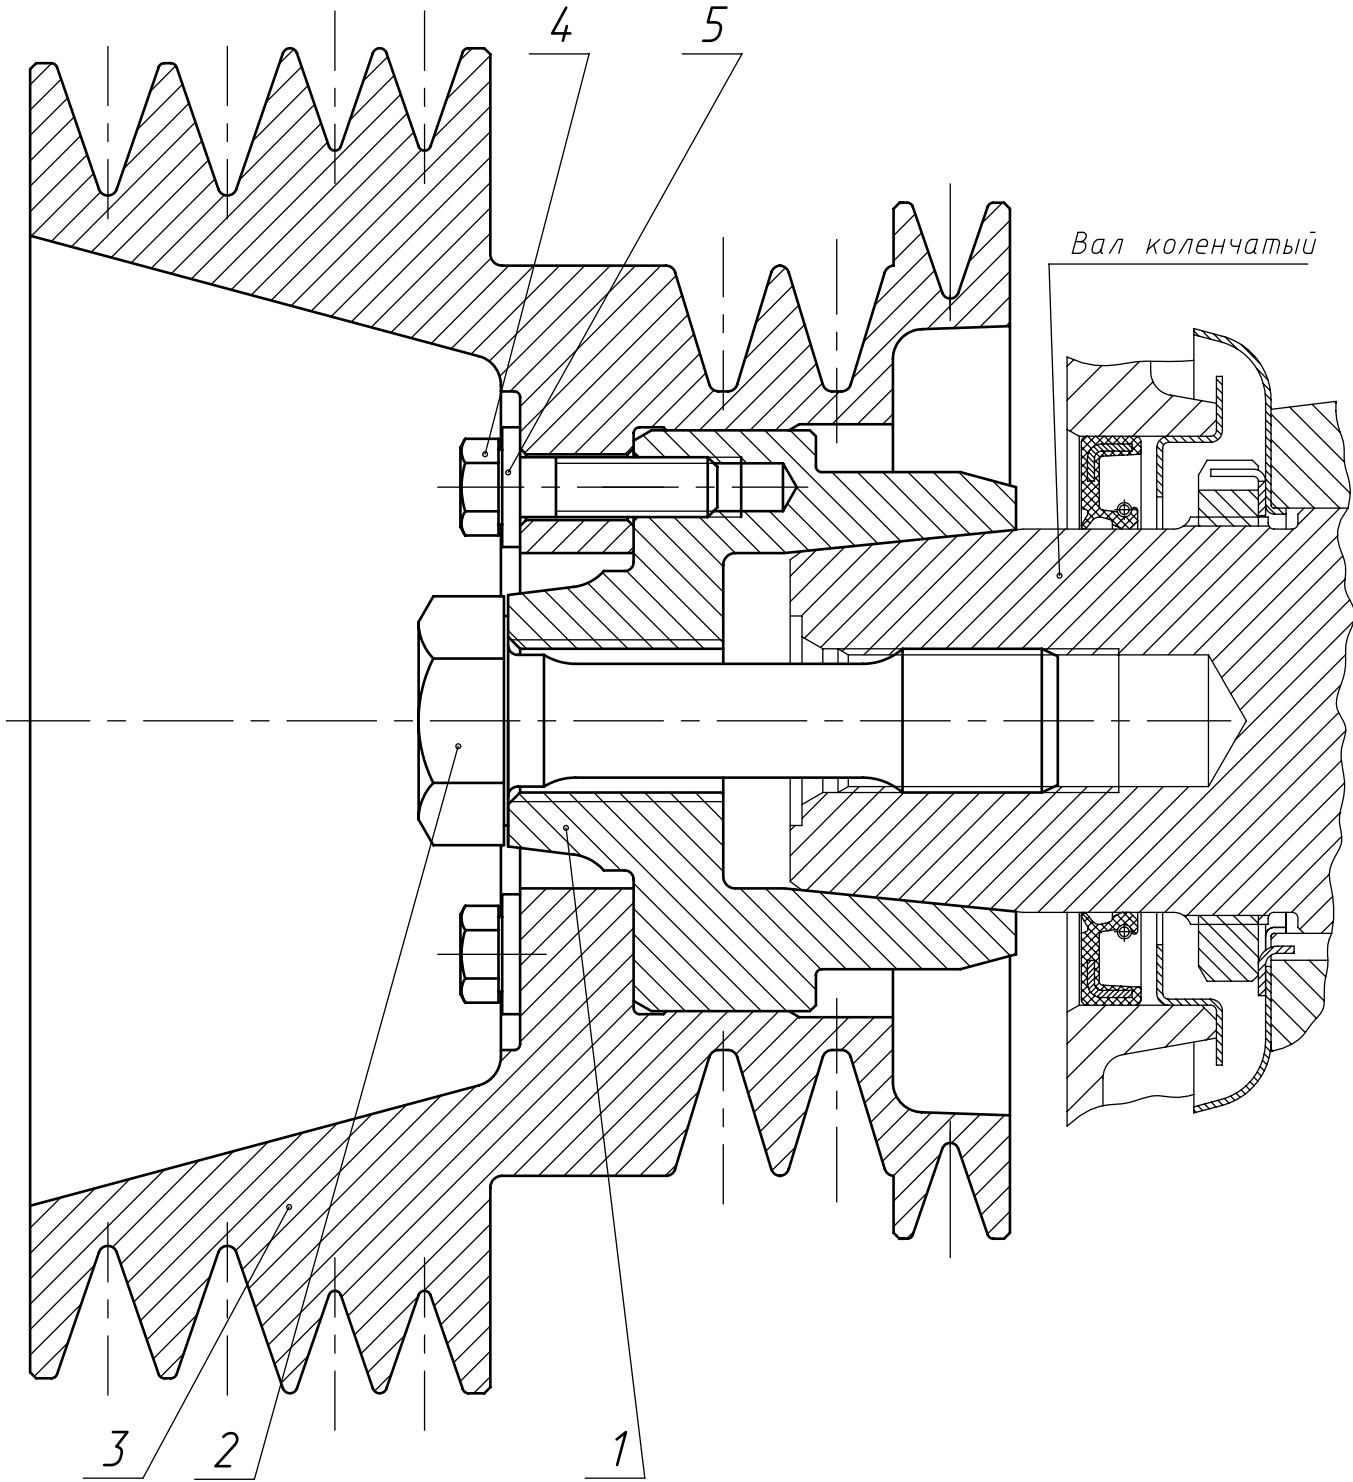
Установка шкива на коленчатый вал двигателя 7601
